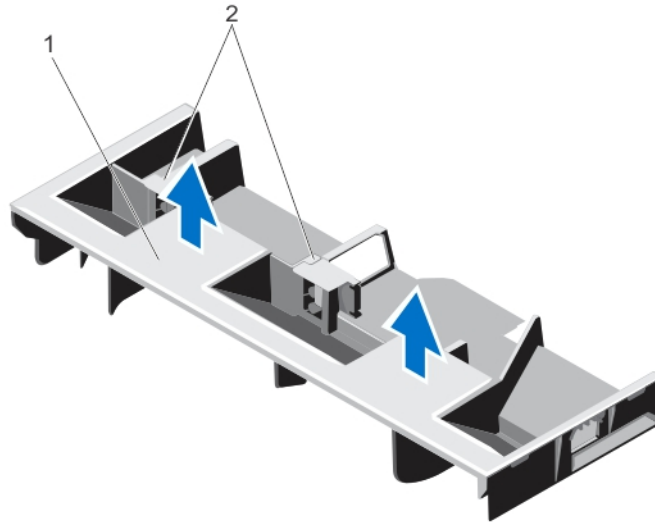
Entfernen und Einsetzen des Kühlgehäuses
